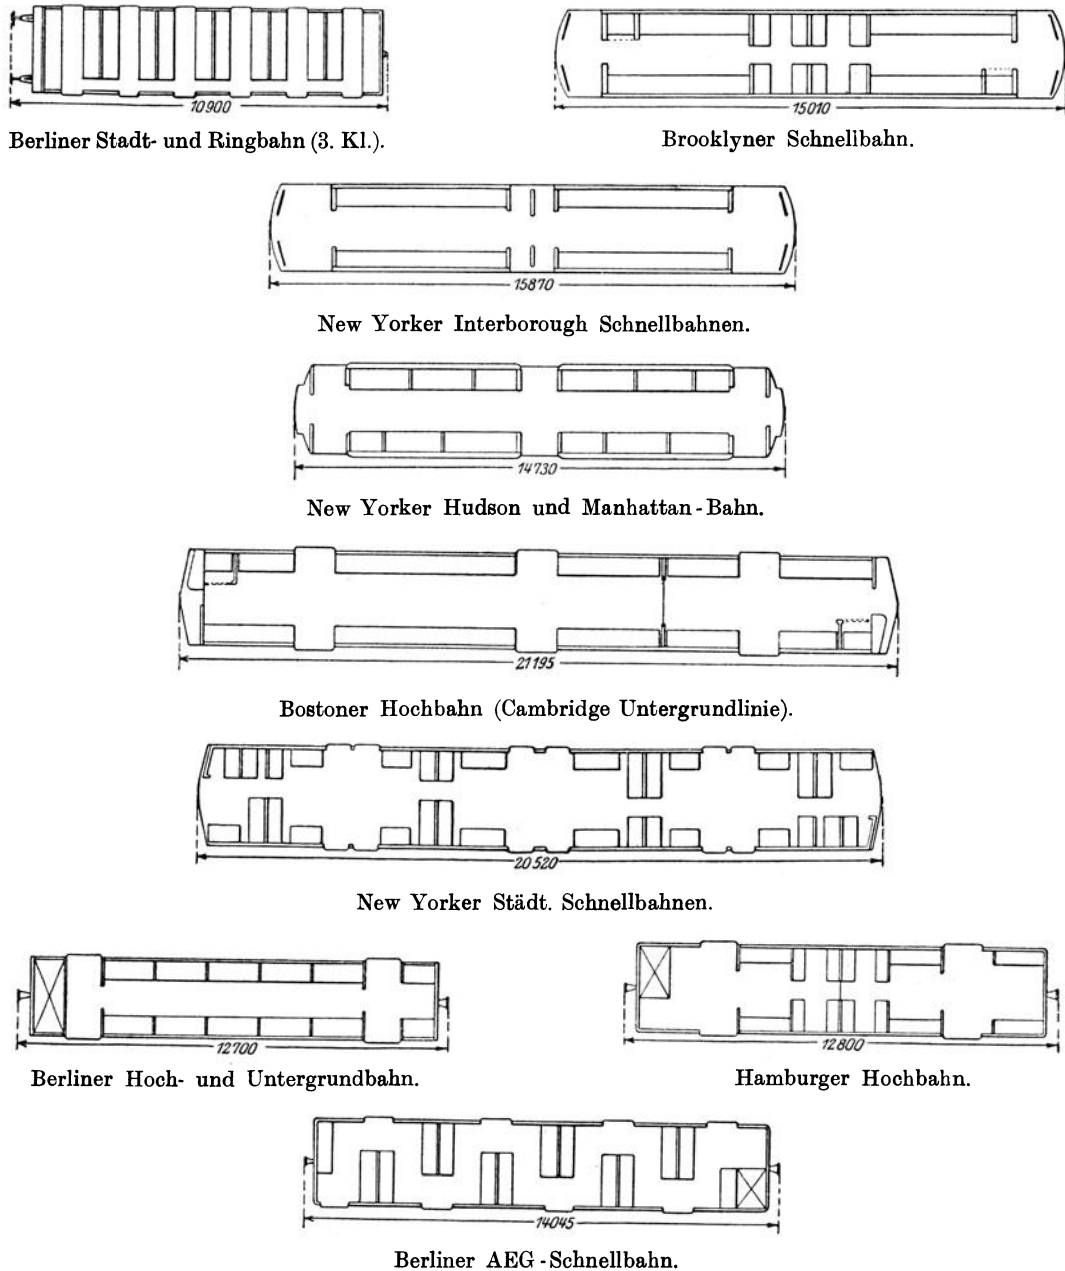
Grundrisse, Sitz- und Türanordnungen von Stadtbahnwagen.
